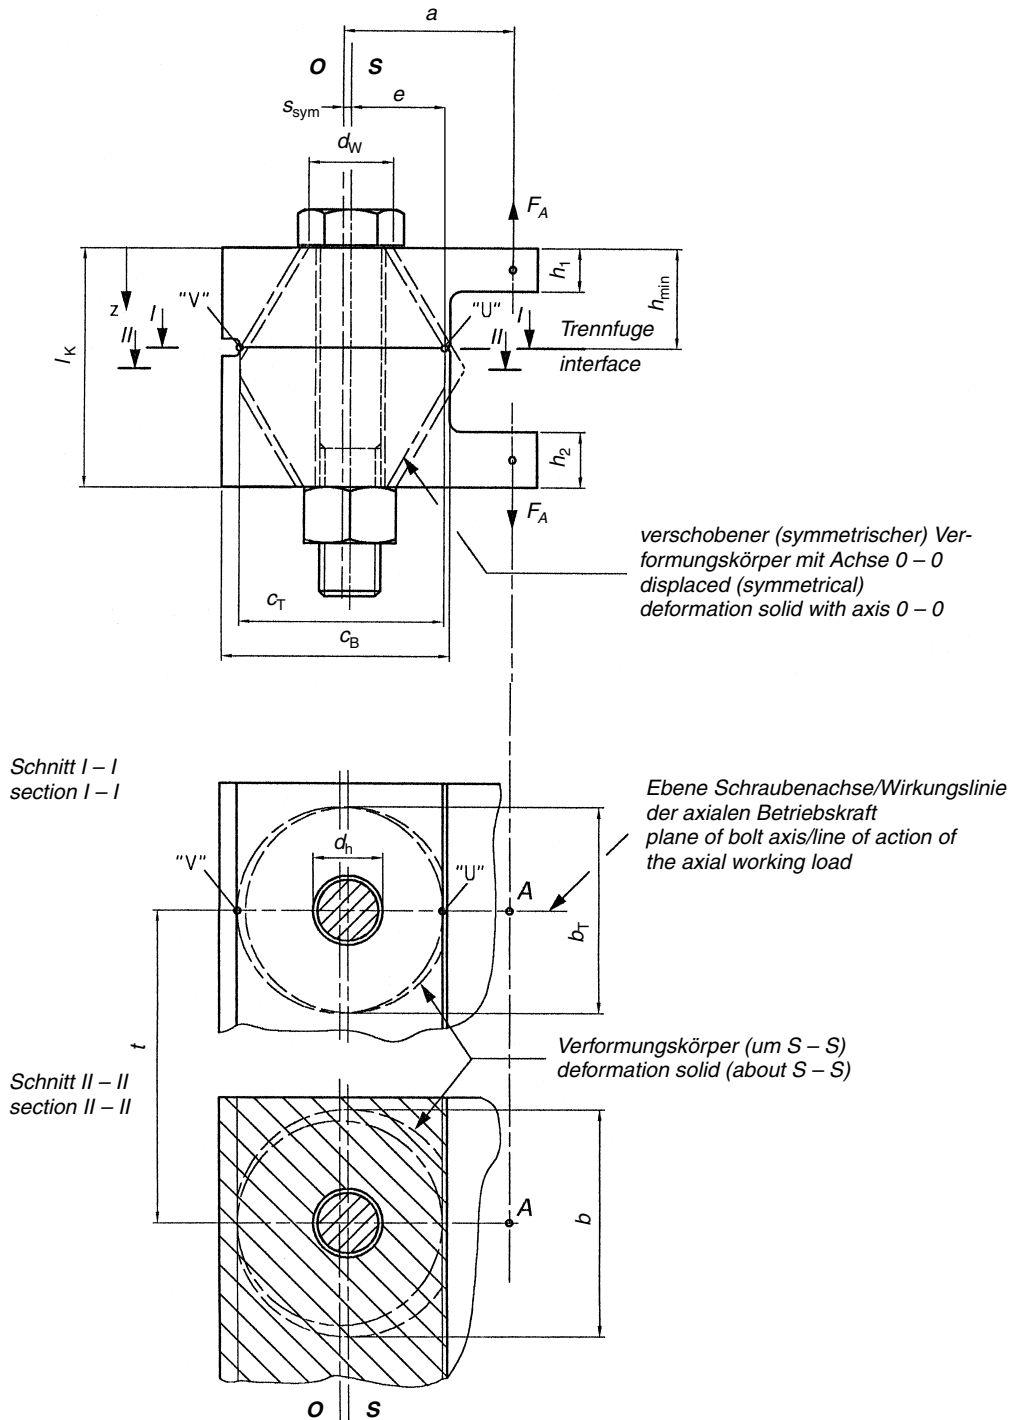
/8. Belastete prismatische Grundkörper einer DSV mit Trennfugenflächen und Anschlusskörper (vereinfachte Darstellung ohne Ersatz-Außendurchmesser D_A)
